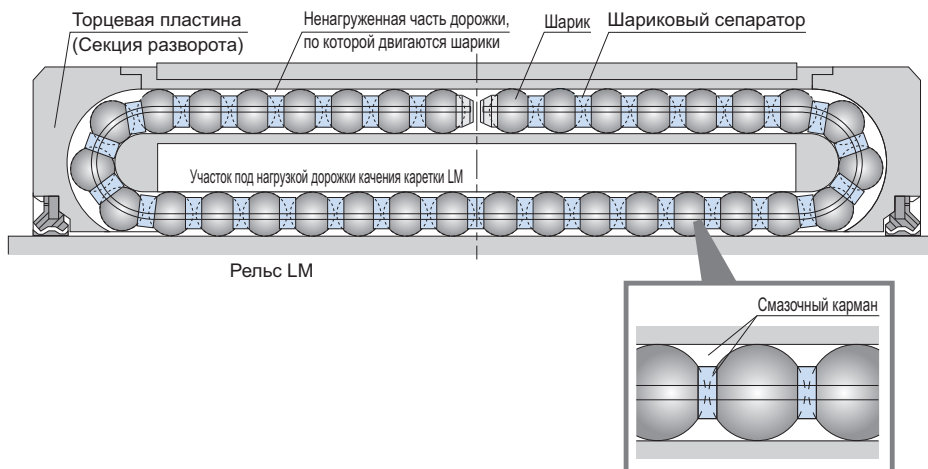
Схема движения элементов внутри каретки LM шариковой рельсовой направляющей LM с сепаратором
